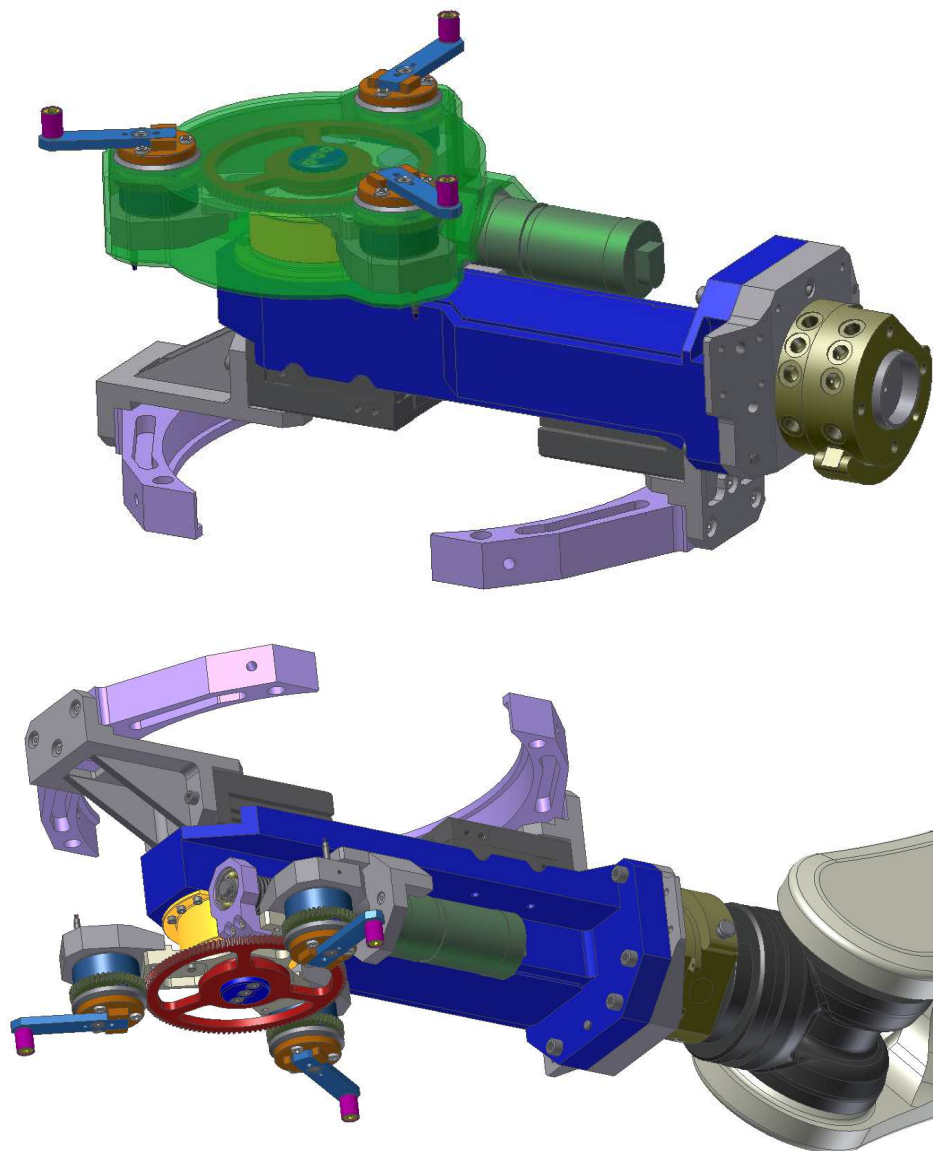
Immagini Cad del gripper, con e senza carter di protezione.
